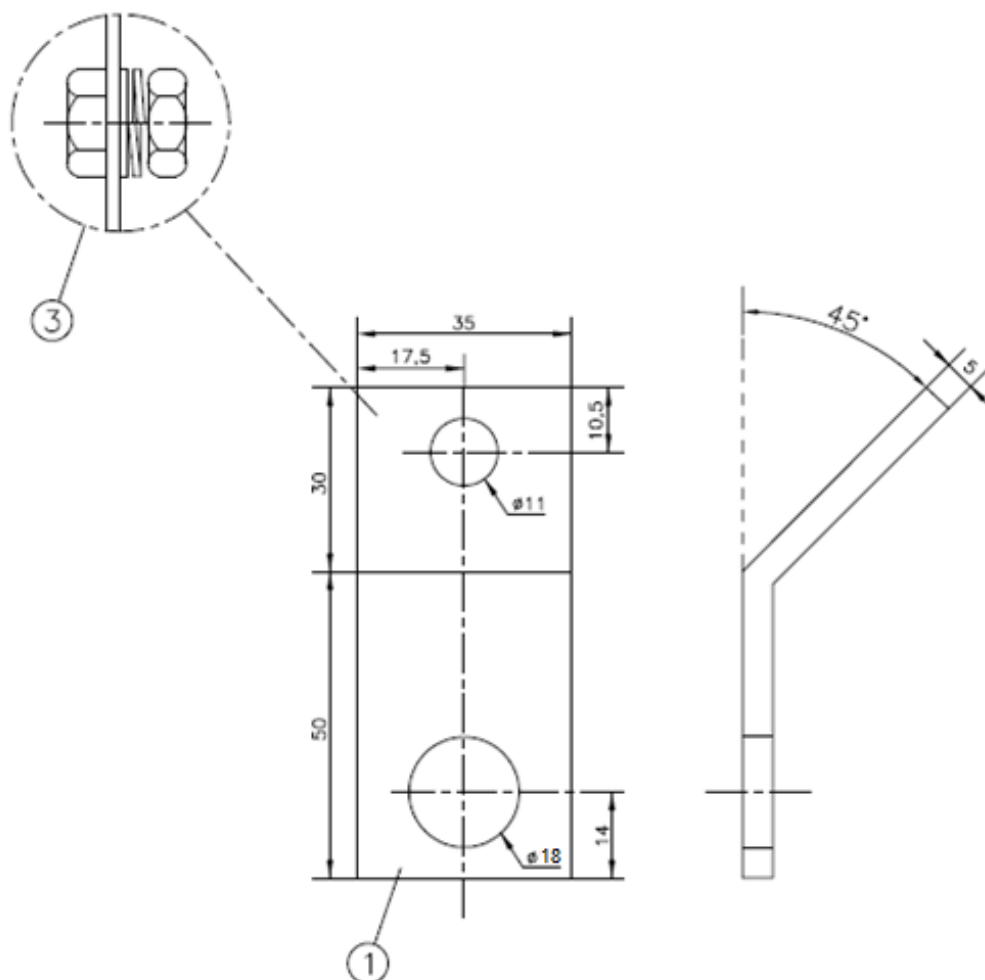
Chapa de aço galvanizado (1), com pormenor de ligação à terra (3)
